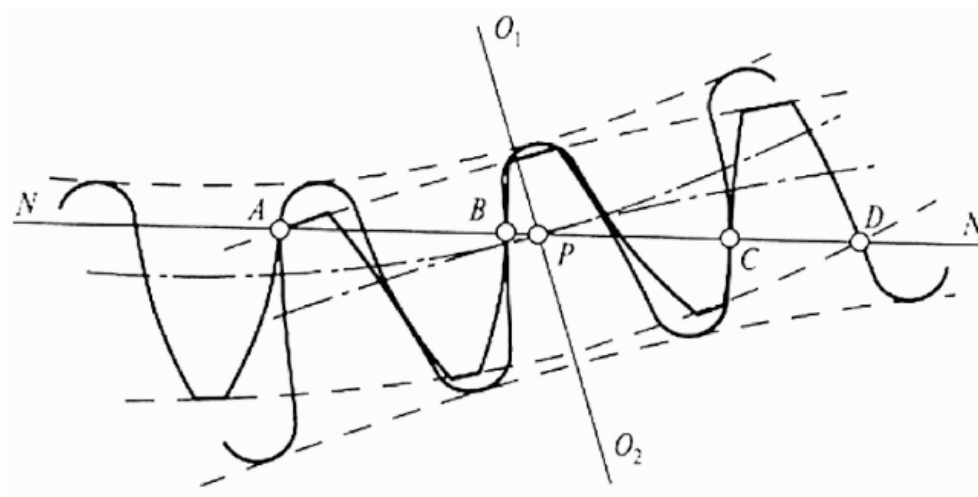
Схема многопарного зацепления зубчатых колес
